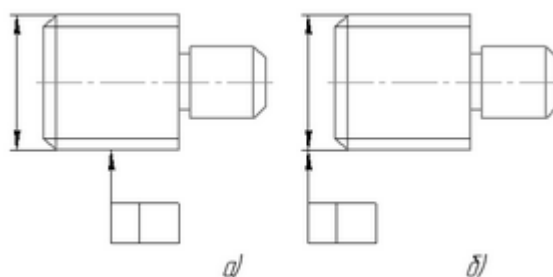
Варианты нанесения допуска на деталях с резьбой
